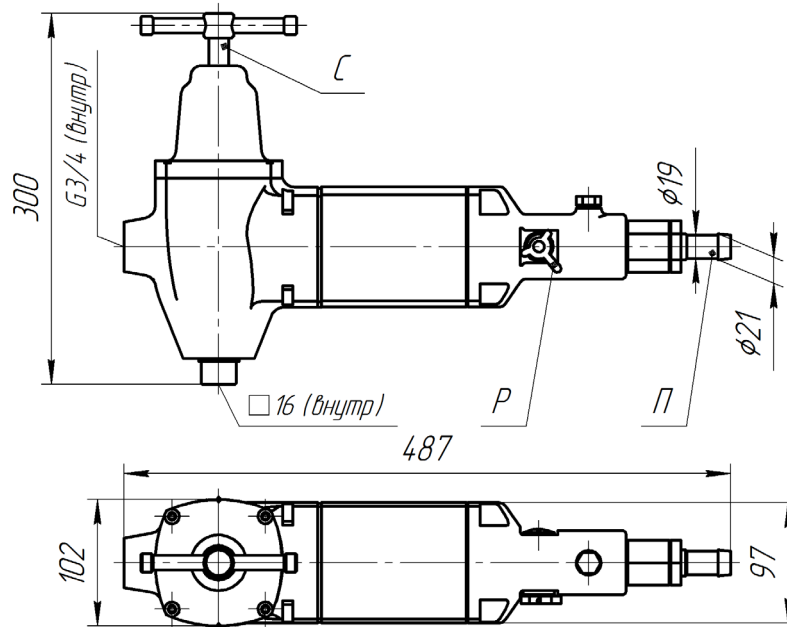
Загальний вигляд пневматичної машини ХТ 7809-0527
